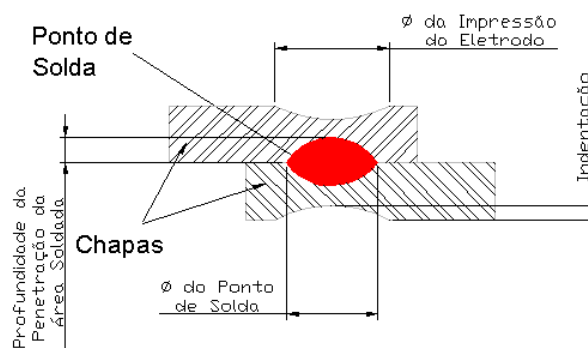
Característica do ponto de solda (AGASHE, WELDING JOURNAL, JULHO 2003,).
